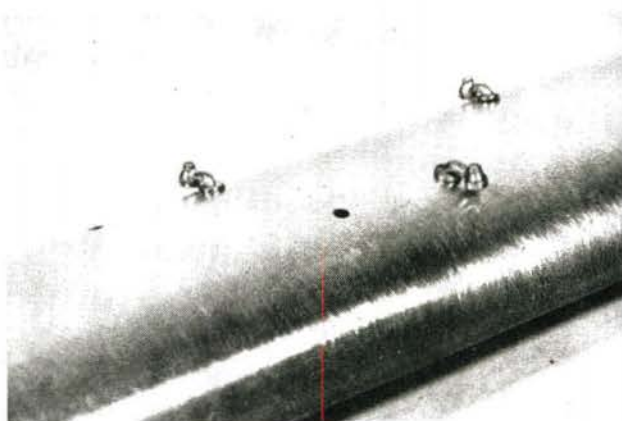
Die Dachlüfter werden auf dem Dach in entsprechende Bohrungen eingeklebt
